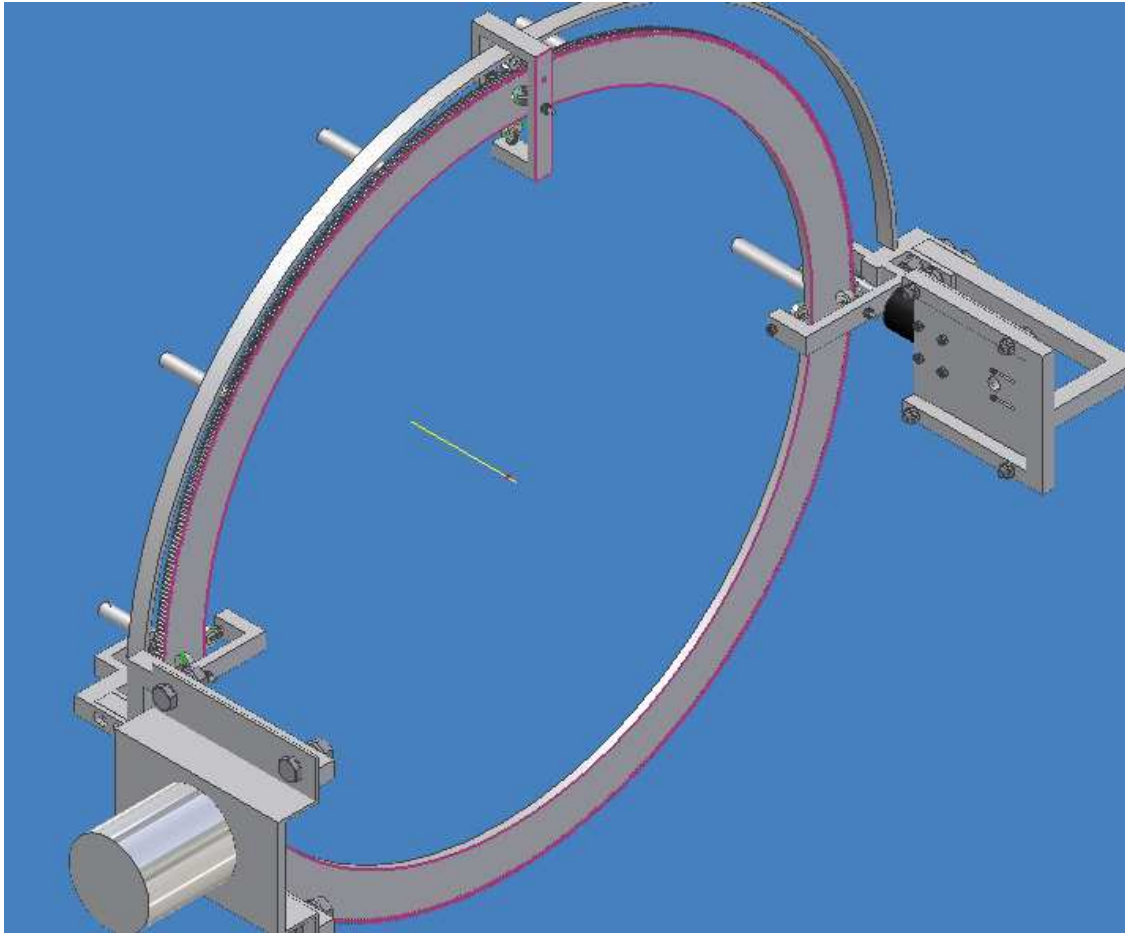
Vista isométrica superior izquierda del equipo mecánico-nucleónico
